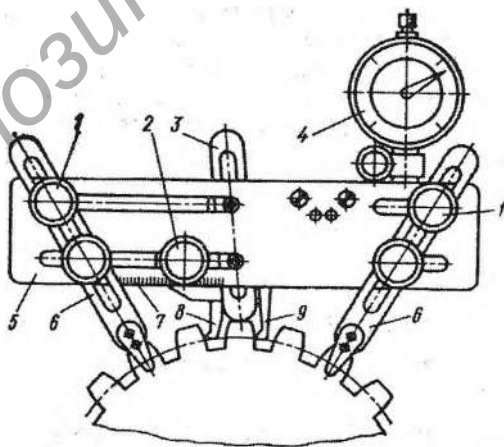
Шагомер для измерения шага зубчатого колеса [10, с. 303]
